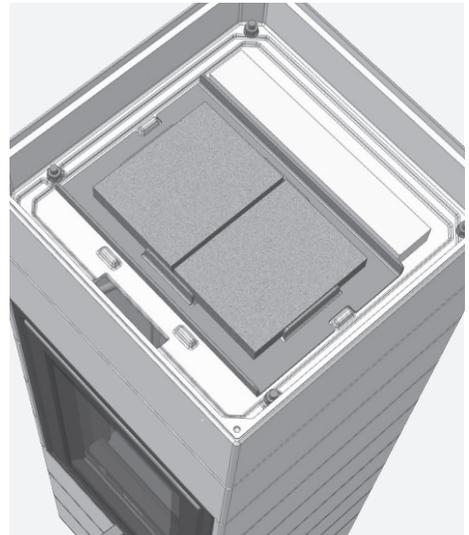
Position des plaques de catalyseur du CORNA tec, vue de dessus, couvercle ôté
